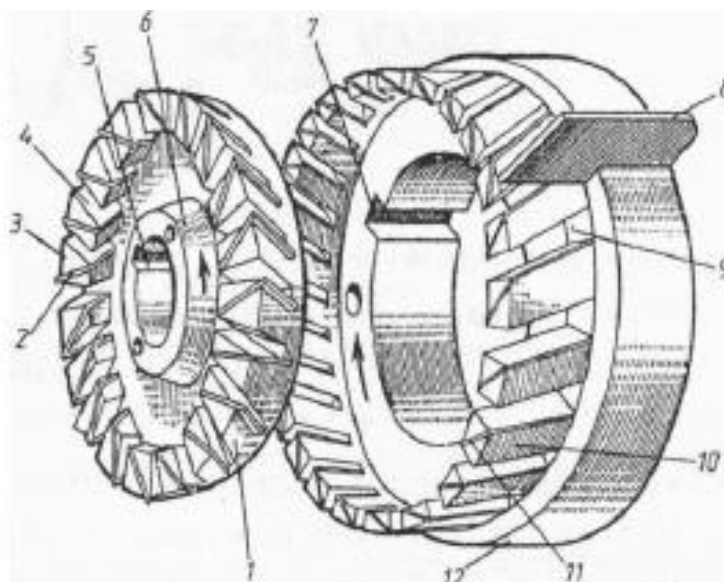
Рабочие органы режущего механизма эмульсатора
